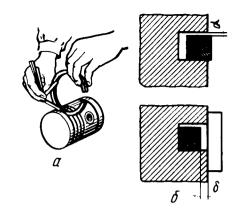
Проверка зазоров в сопряжении поршневое кольцо — канавка поршня:
